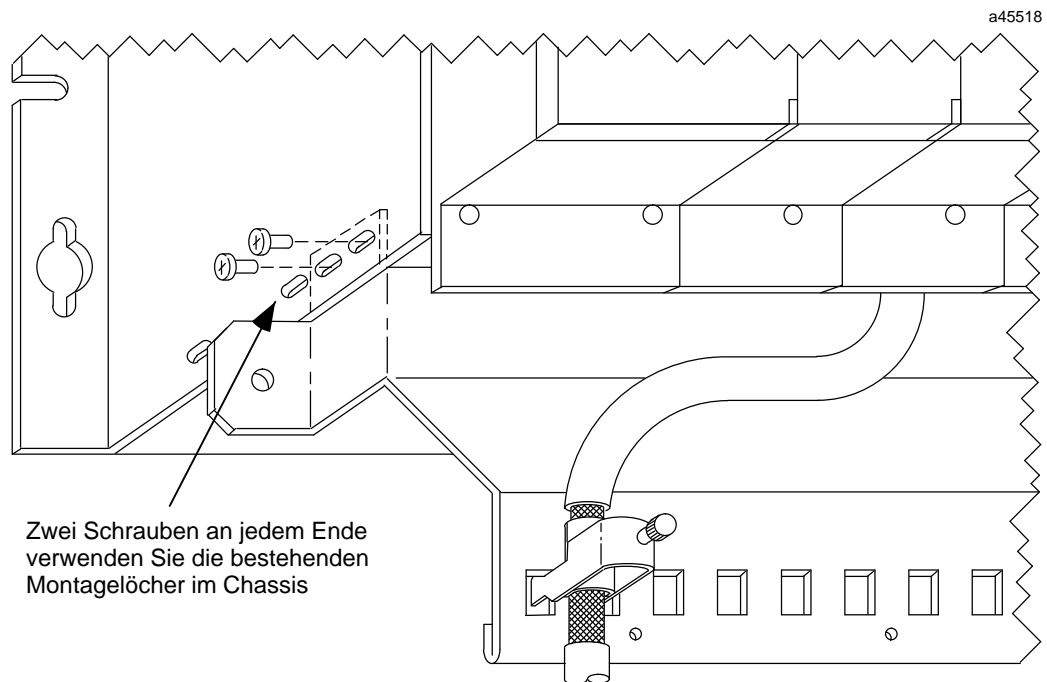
Kabelschirmbefestigung am SPS-Chassis der Serie 90-70
